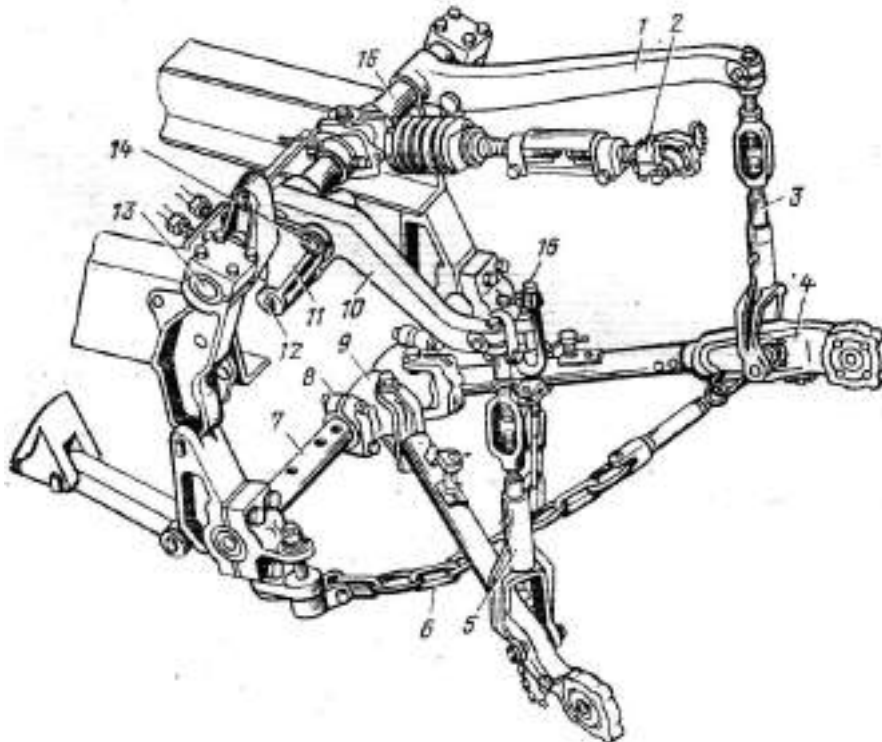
Механизм навески трактора Т-150К, налаженный по двухточечной схеме:
